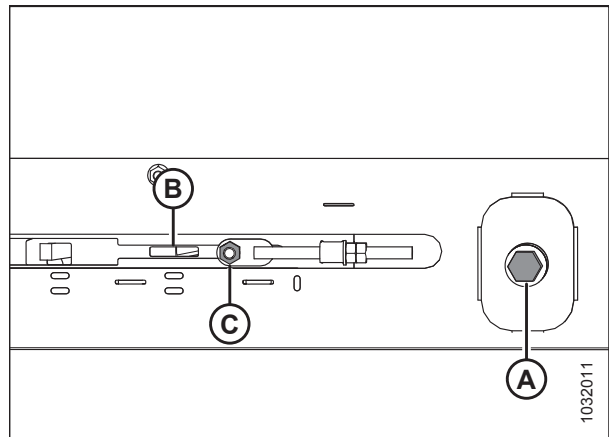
Ajustador de tensión: se muestra el lado izquierdo; opuesto al lado derecho
